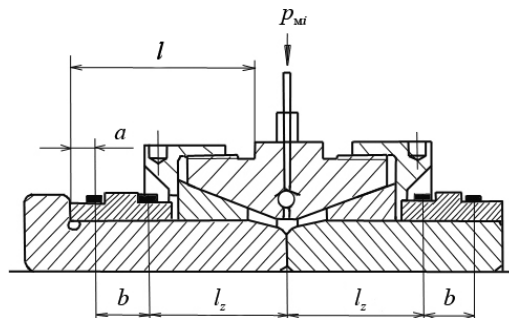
Общий вид устройства для реализации разработанного метода неразрушающего контроля прочности напрессовки внутренних колец буксовых подшипников на шейки осей колёсных пар вагонов (патенты ВУ 13116 С1, RU 2329478 С1)
